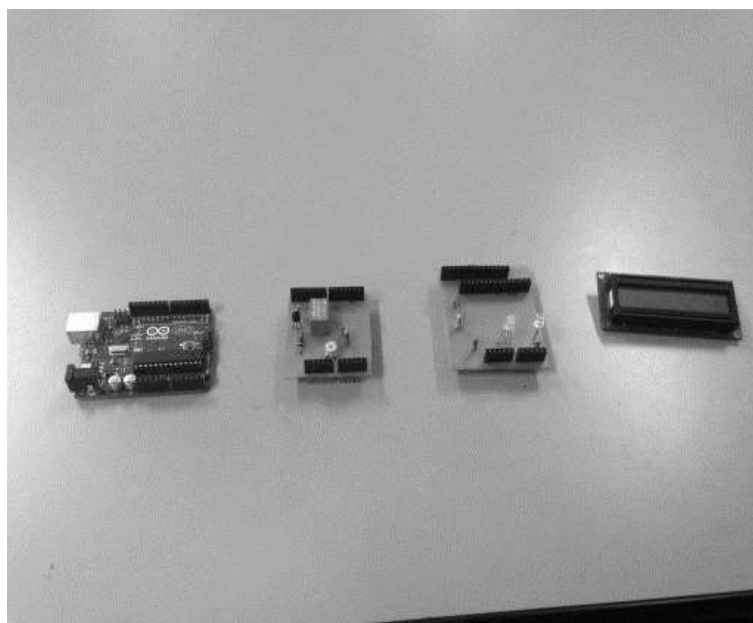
Ensamble de los componentes electrónicos en las PCB.
